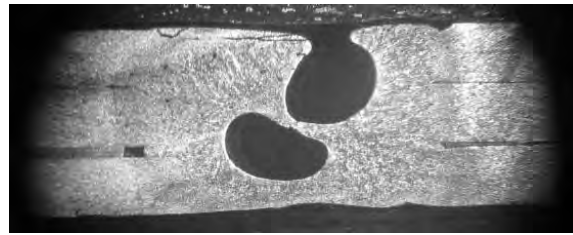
Макрошлиф пакетного рельефного сварного соединения пластин с дефектами
